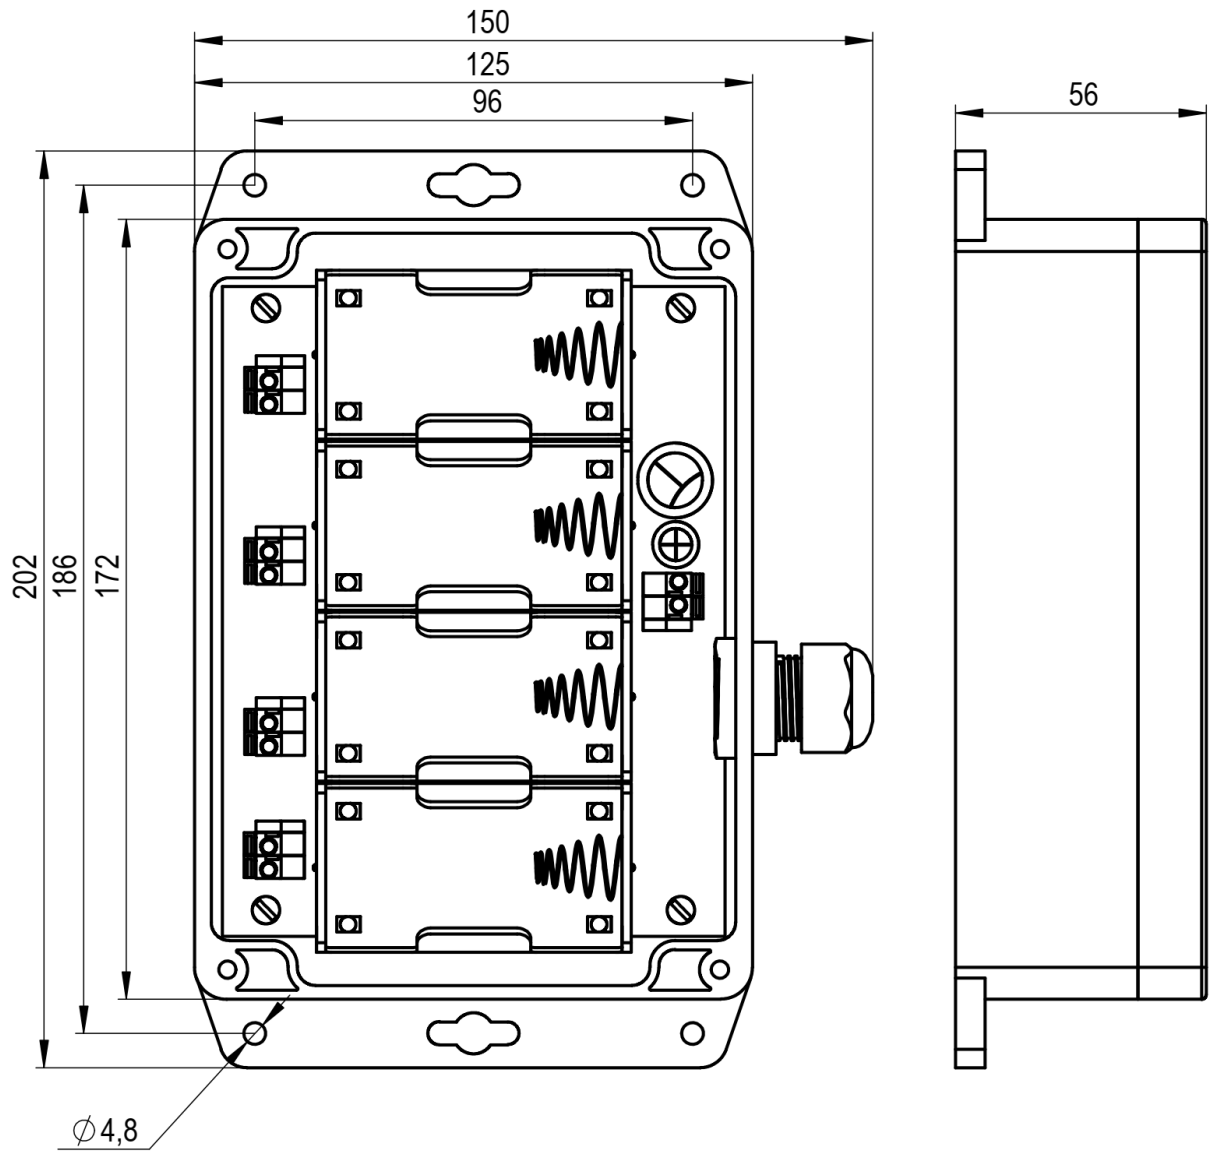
Габаритные и установочные размеры блока батарейного питания ПБ-4
